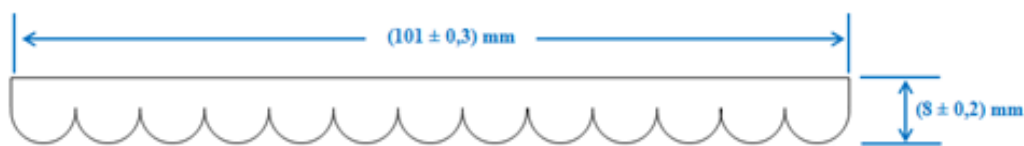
Dimensionamiento de la sobretapa, vista lateral.
